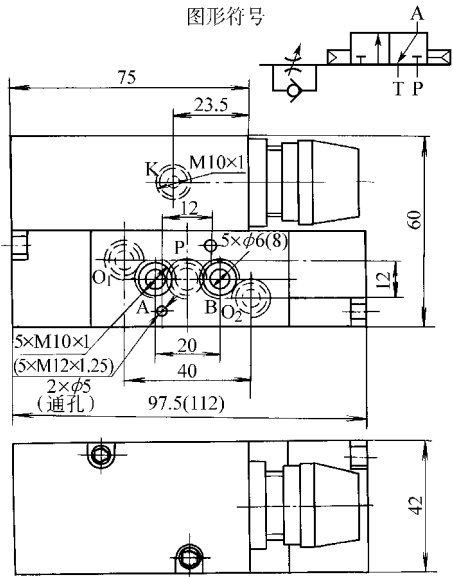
K25Y-L6(8)-J 型二位五通延时换向阀外形尺寸
